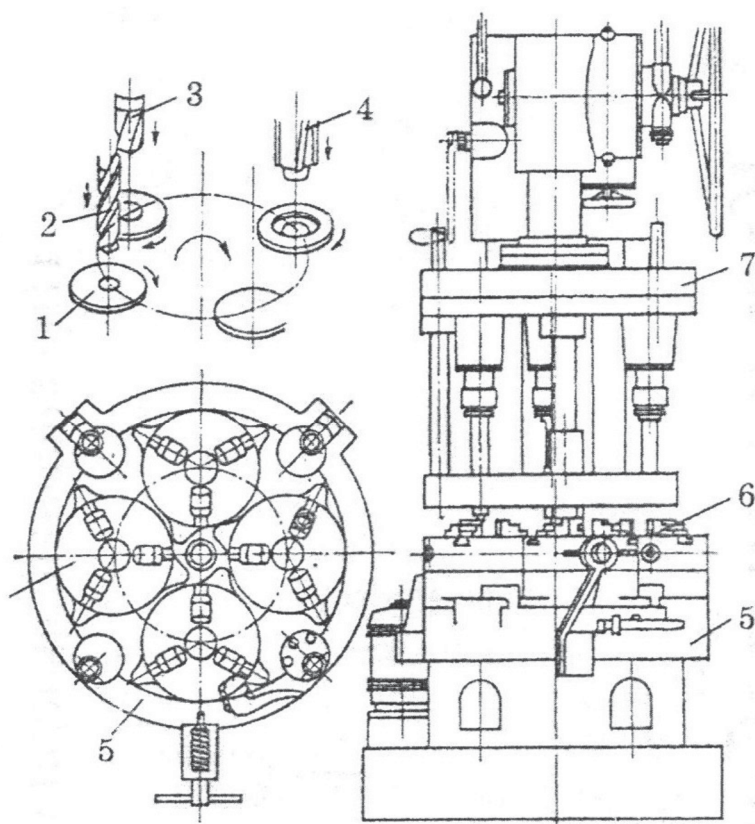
Схема обработки отверстия трехшпindleйной головкой на сверлильном станке с поворотным столом: 1 – заготовка; 2 – сверло; 3 – сверло; 4 – зенкер; 5 – стол; 6 – приспособление; 7 – сверлильная головка
